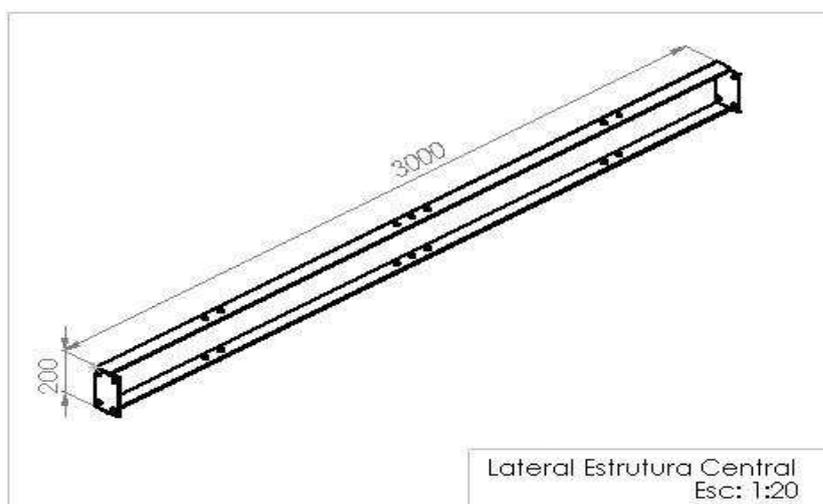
Perfil Planificado Lateral Estrutura Central TC16" Remodelada
